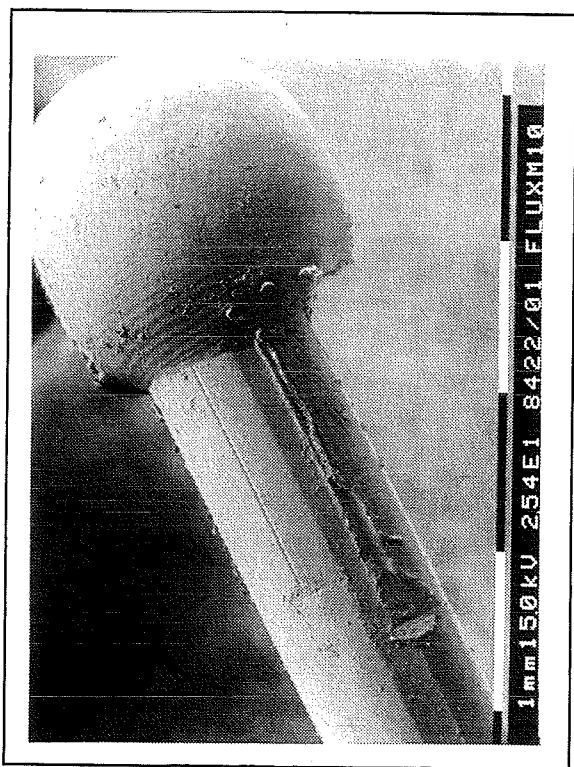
beschadiging op de lasdraad fluxofil, 25 X vergroot.
